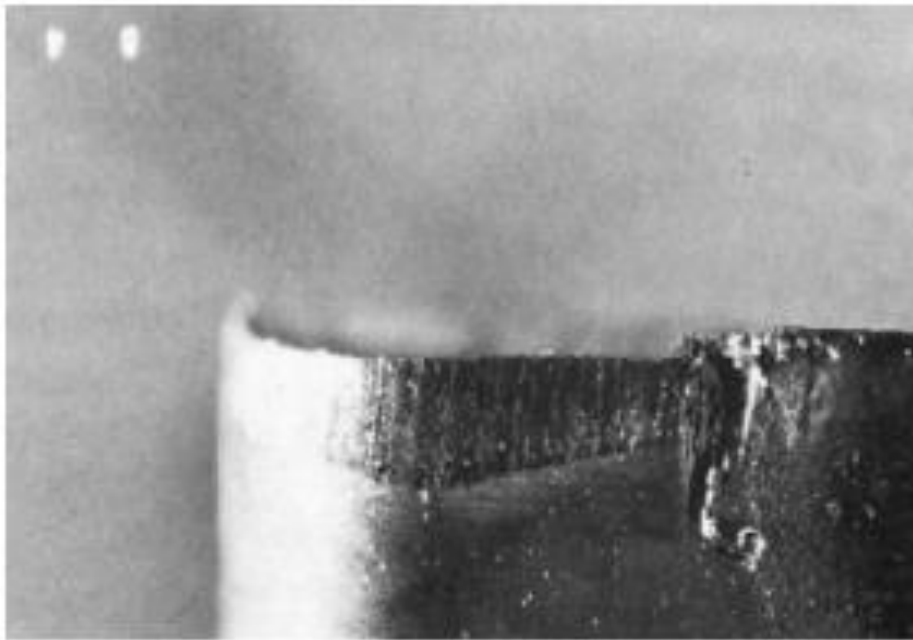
Desgaste de flanco na superfície de saída de uma ferramenta (Introdução aos processos de usinagem, 2010)
